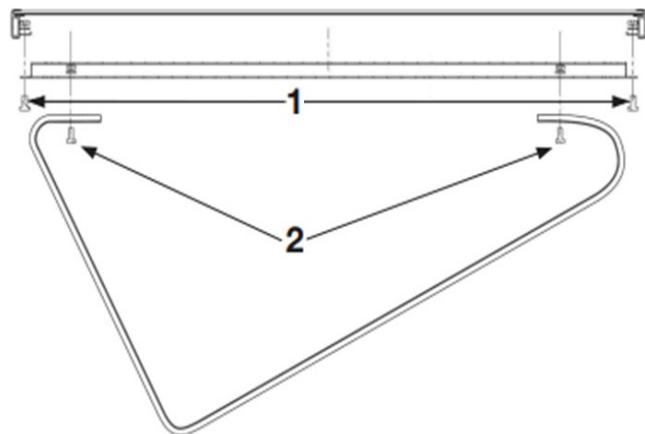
Detailansicht für die Montage mit Standfüßen (Back-Rail und Modul-Querschnitt von oben)
